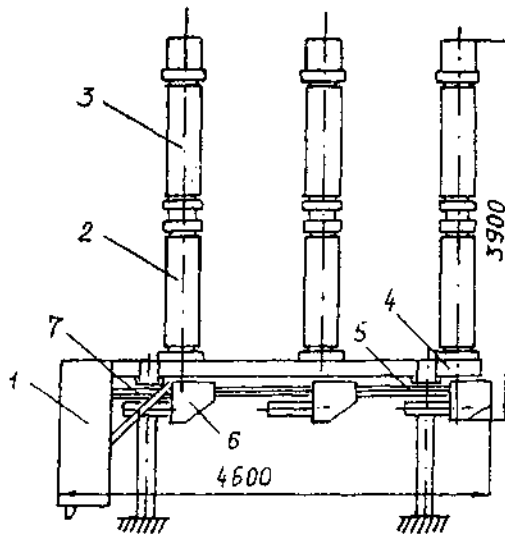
Выключатель ВМТ-ПОБ: 1 — привод; 2— опорный изолятор; 3 — дугогасительное устройство; 4 — рама; 5, 7 — труба; 6 — механизм управления
